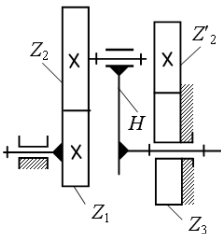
Планетарный механизм с двумя внешними зацеплениями
